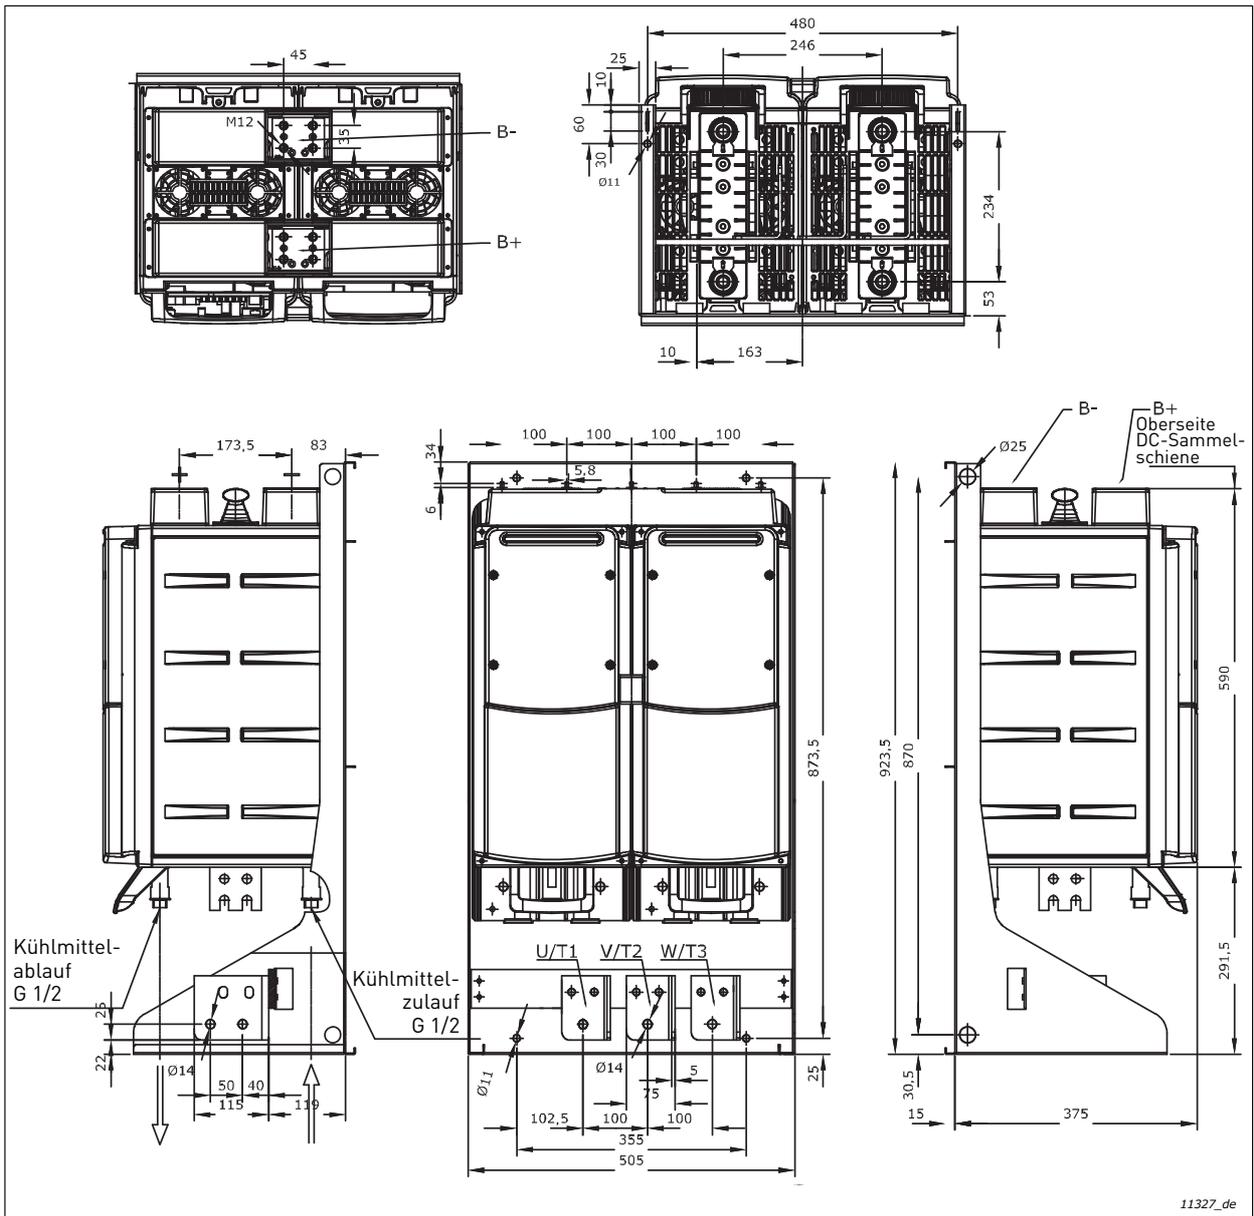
Flüssiggekühlter VACON®-Wechselrichter mit Montagegestell (CH63)
